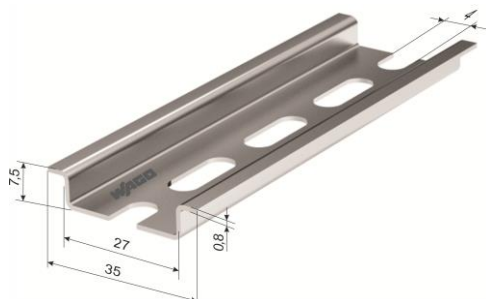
Внешний вид и размеры DIN-рейки Wago
